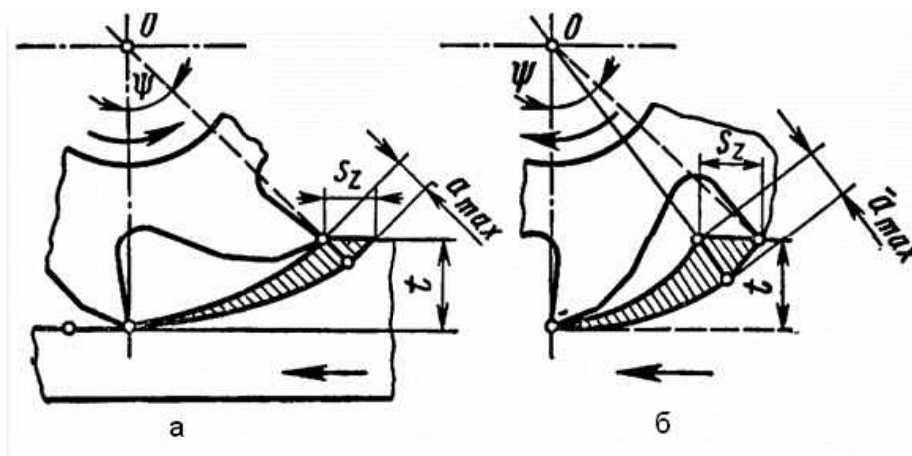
Схеми фрезерування: а – зустрічне; б – попутне
